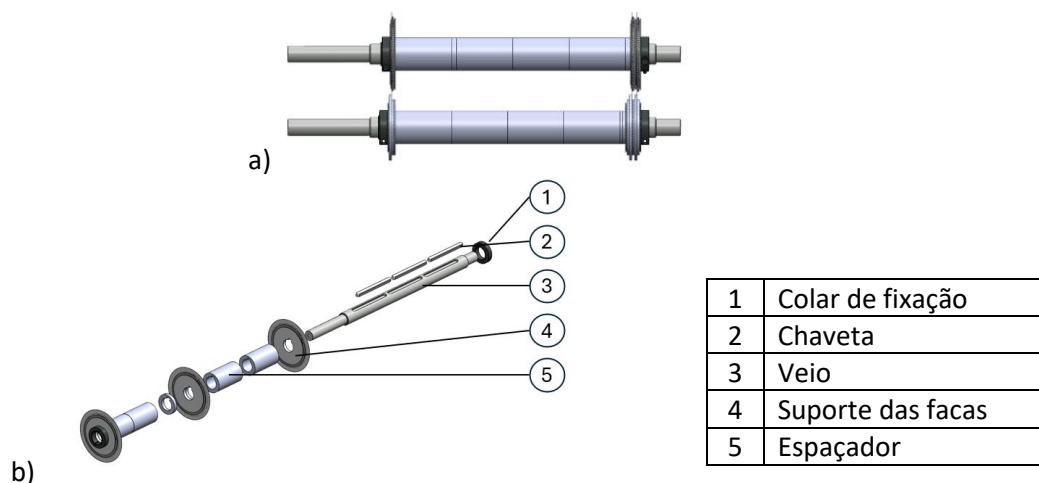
Solução 1: a) vista frontal; b) vista explodida.
